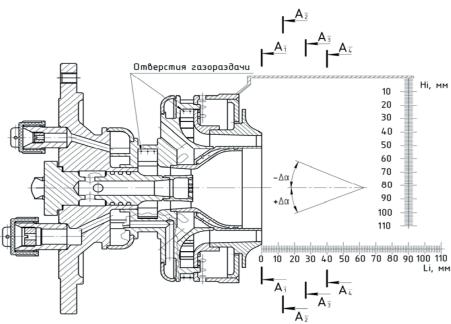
Конструктивная схема низкоэмиссионного горелочного устройства и координаты расположения сечений
